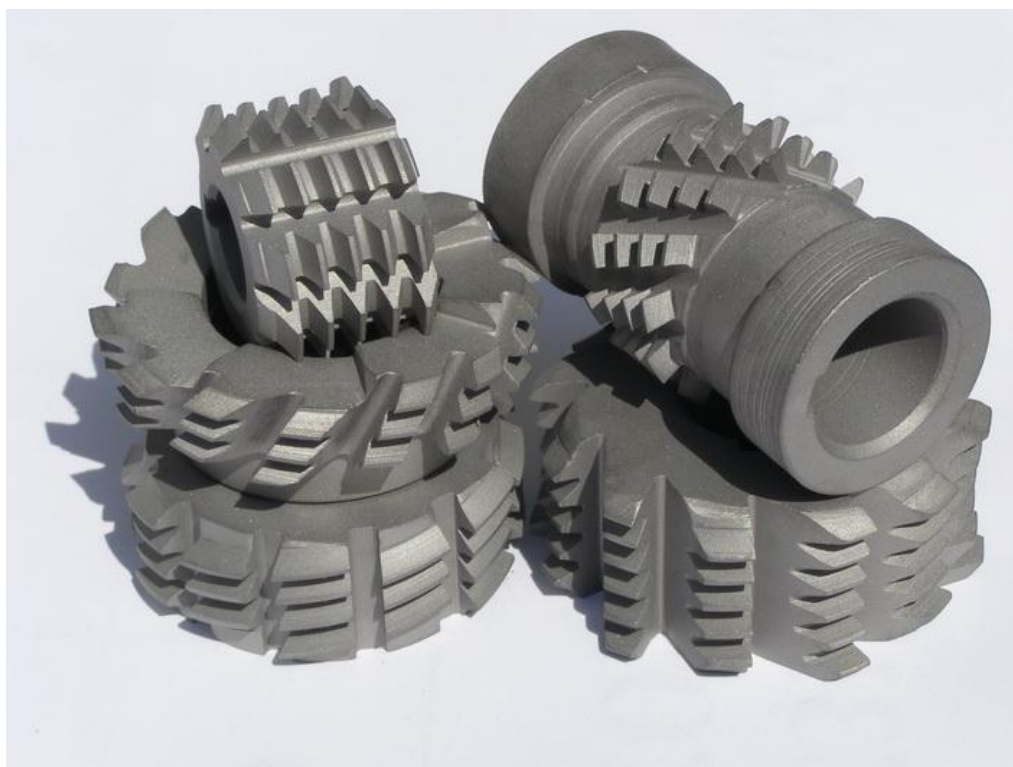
Фото гіперболоїдних фрез для нарізування циліндричних зубчастих коліс
